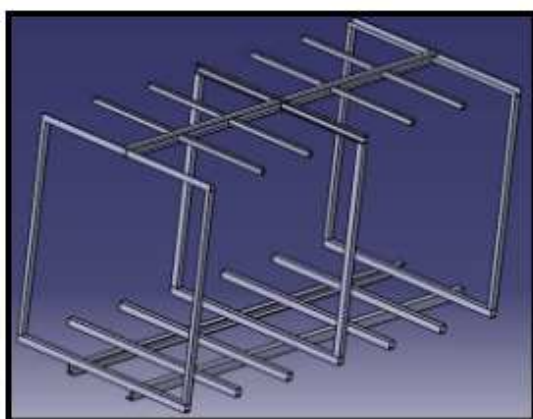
8: Estructura fija. Detalle travesaños superiores
